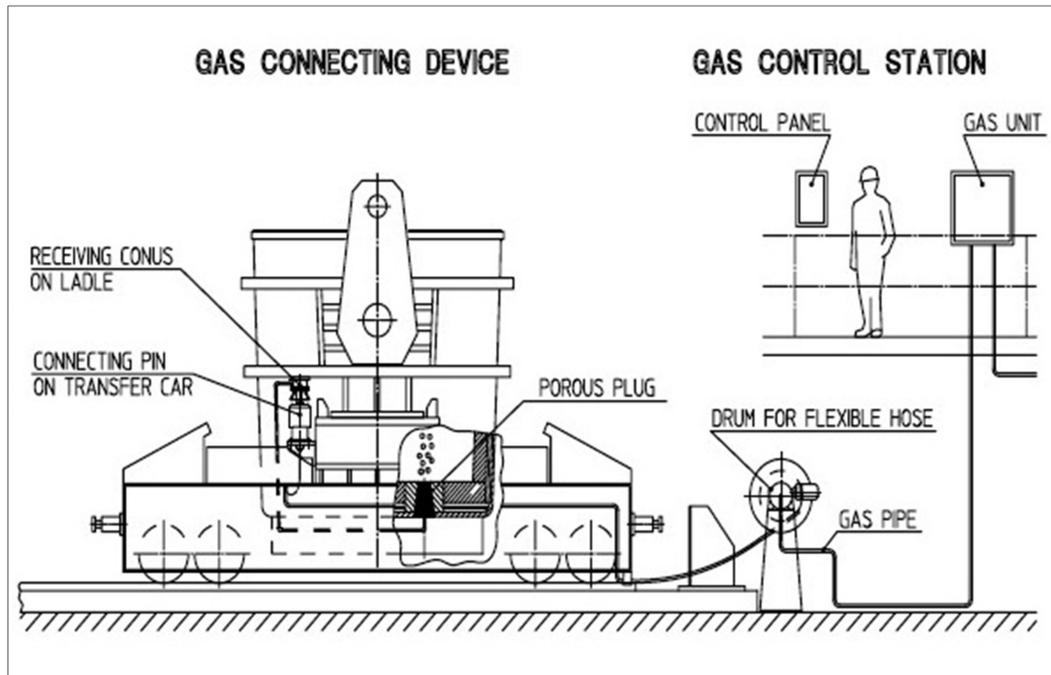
Vista en plano del Sistema de Inyector de gas Argón.
